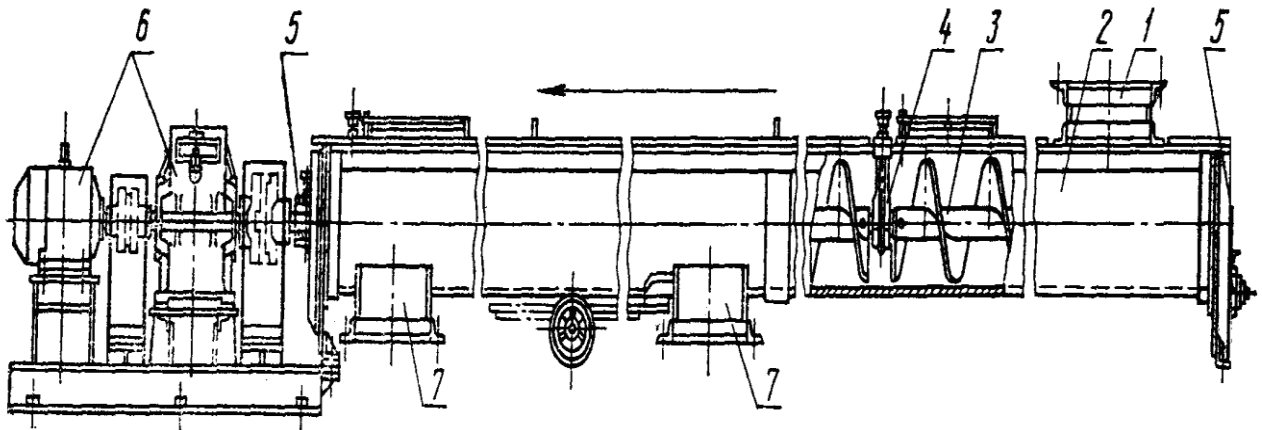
Гвинтовий конвеєр: 1 - завантажувальний патрубок; 2 - жолоб; 3 - гвинт; 4 - проміжний підшипник; 5 - кінцевий підшипник; 6 - привод; 7 - розвантажувальні люки.
